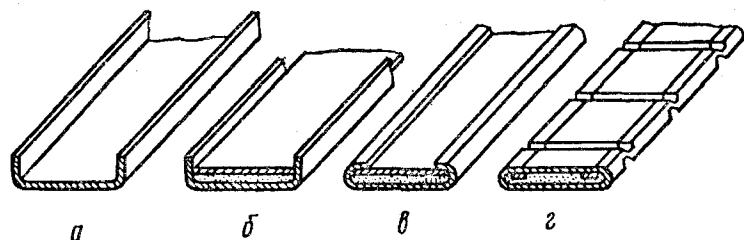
Схема изготовления порошковой ленты: а — отбортовка нижней ленты; б — заполнение порошком и укладка верхней ленты; в — завальцовка кромок нижней ленты; г — выдавливание углублений для уплотнения порошка и придания гибкости порошковой ленте
